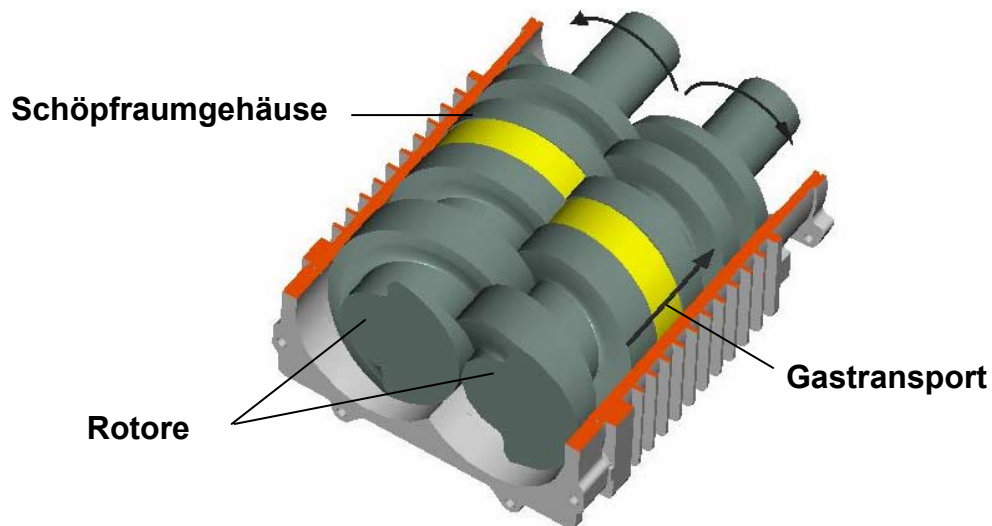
Funktionsprinzip einer Schraubenvakuumpumpe, Rotore mit variabler Steigung
